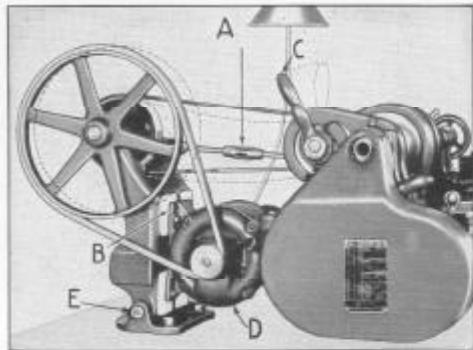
Extremo de un torno de banco con transmisión horizontal ajustable de motor
